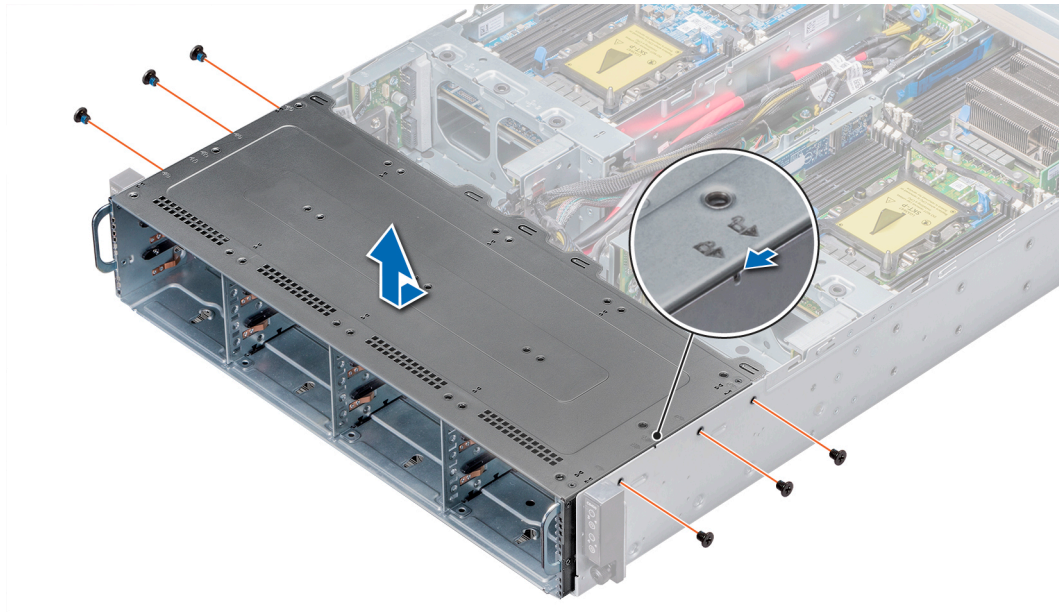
Entfernen des 3,5-Zoll-Laufwerksgehäuses
